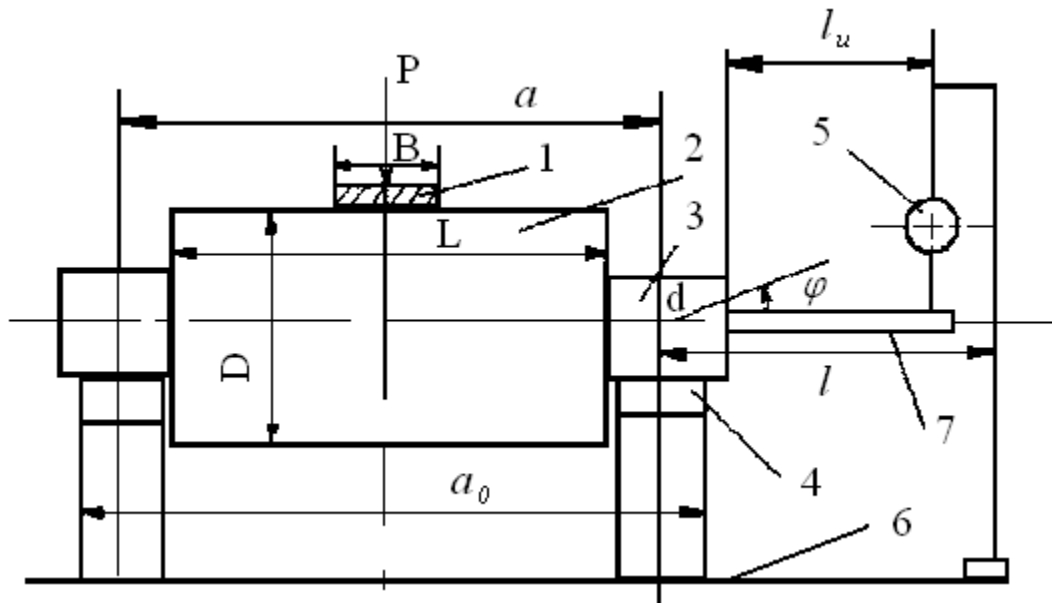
Установка для визначення прогину валка: 1 - смуга; 2 - опора валок; 3 - шийка валка; 4 - опора; 5 - індикатор; 6 - опорна плита.
